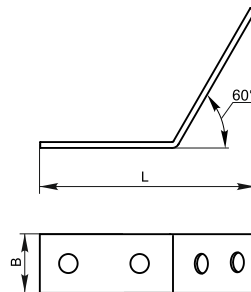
Уголок крепёжный наклонный 60° для STRUT-профиля
